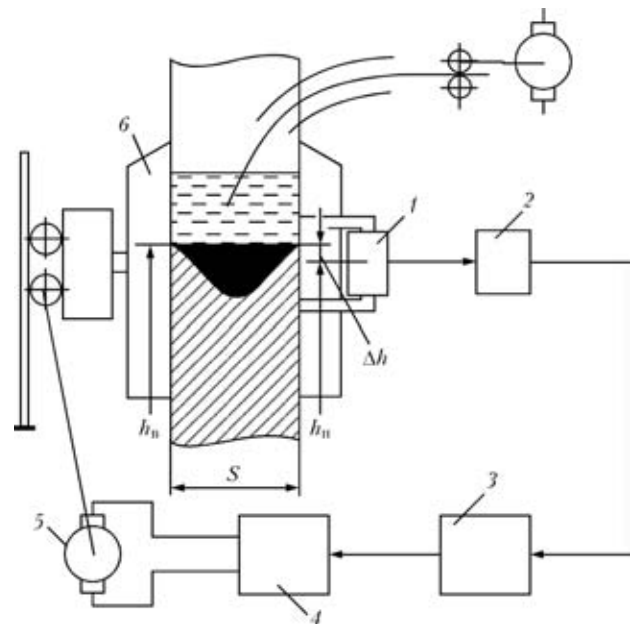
Функциональная схема системы автоматической стабилизации уровня жидкой металлической ванны при ЭШС: 1 — датчик; 2 — измерительный преобразователь; 3 — регулятор; 4 — блок управления двигателем; 5 — двигатель перемещения сварочной тележки; 6 — ползун; h_b — уровень жидкой металлической ванны; h_n — положение ползуна (датчика уровня); Δh — ошибка регулирования уровня ванны
